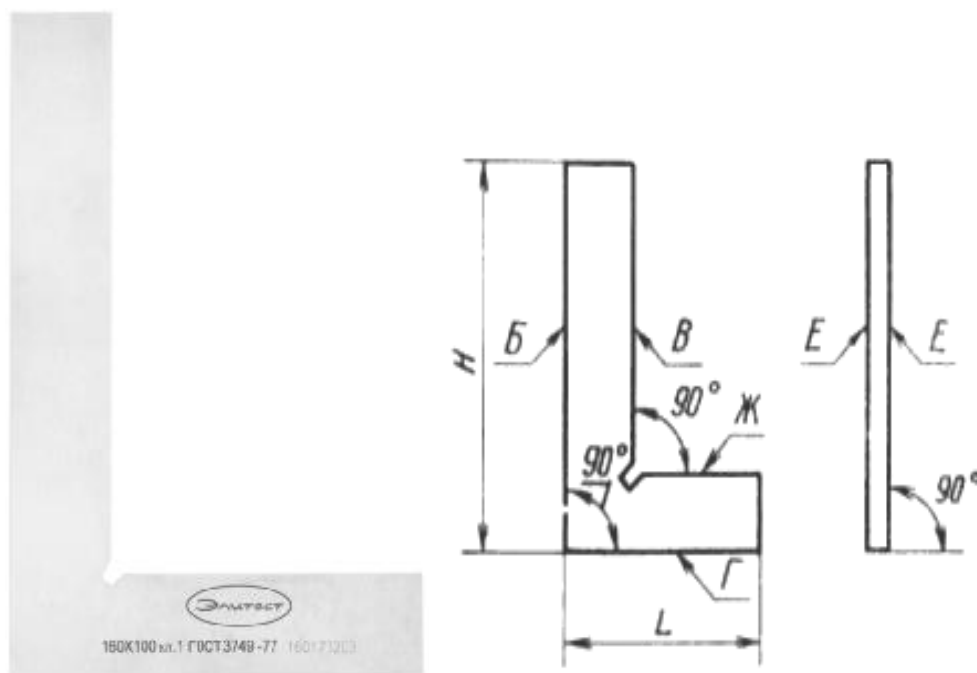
Общий вид угольника слесарного плоского 90° УП «Элитест», обозначение основных размеров и поверхностей
